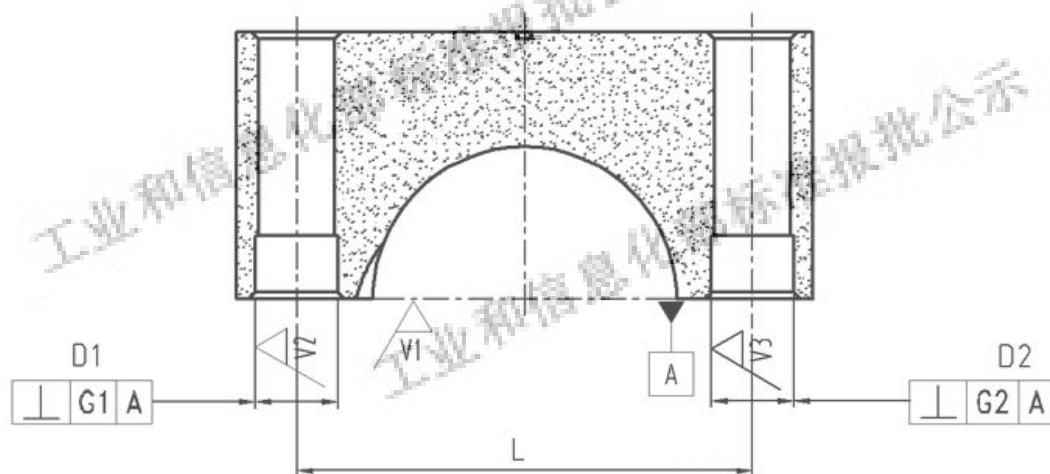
销配式曲轴轴承盖重要尺寸、几何公差及表面粗糙度标注示意图
